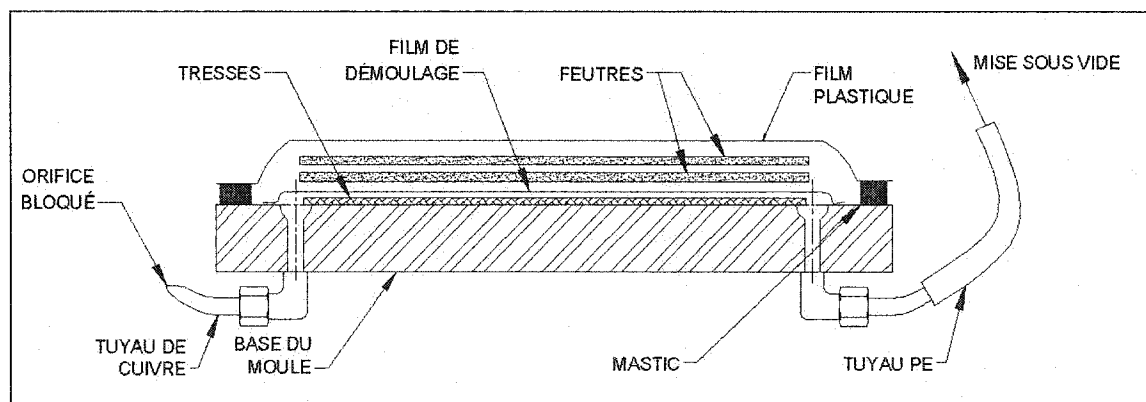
Coupe du montage de fabrication de la plaque à fibres unidirectionnelles
